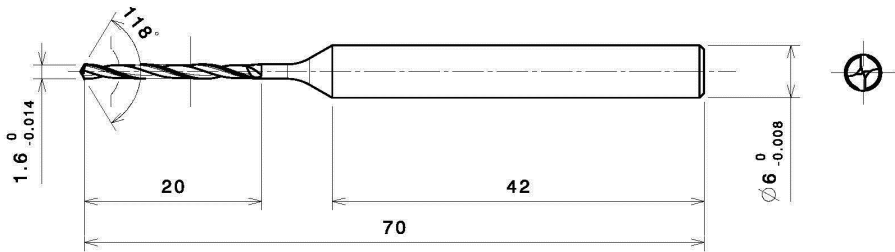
Креслення твердосплавної фрези SSD D1.6X20FX 70-6 із сплаву UF10
